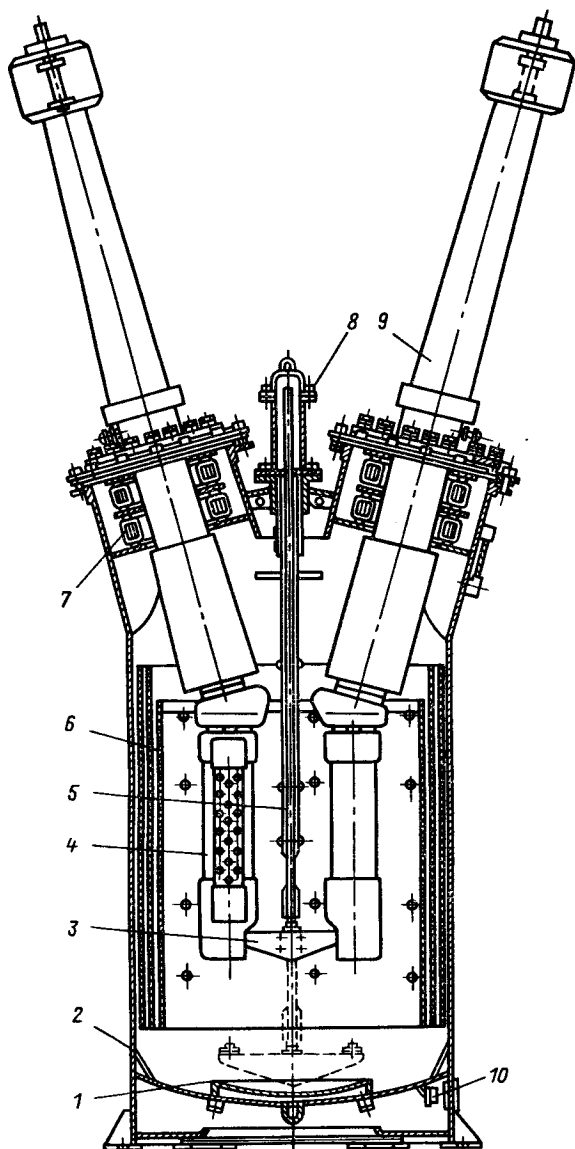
Полюс бакового выключателя У-220-2000-40У1
